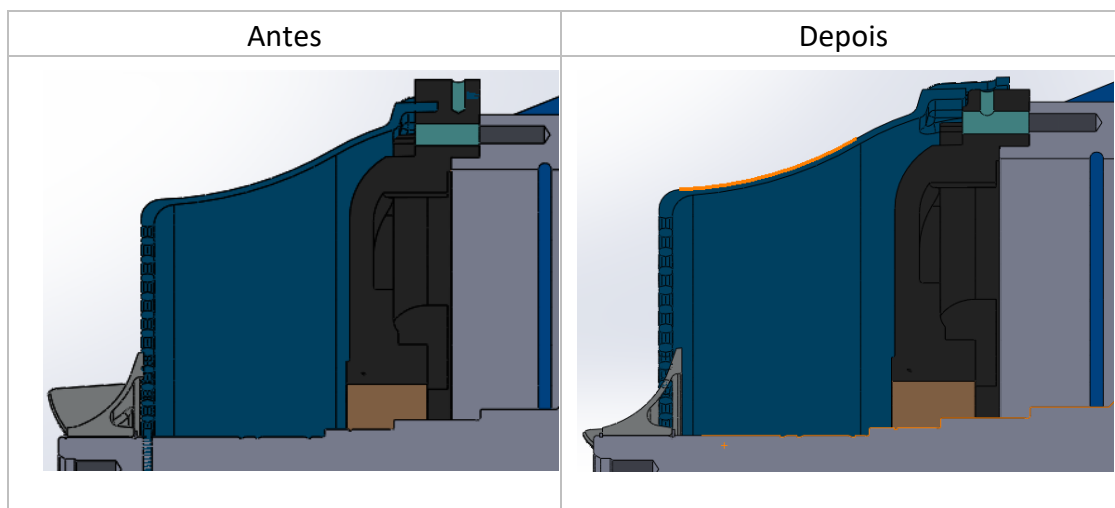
Antes e depois da Tampa Traseira ser maquinada
